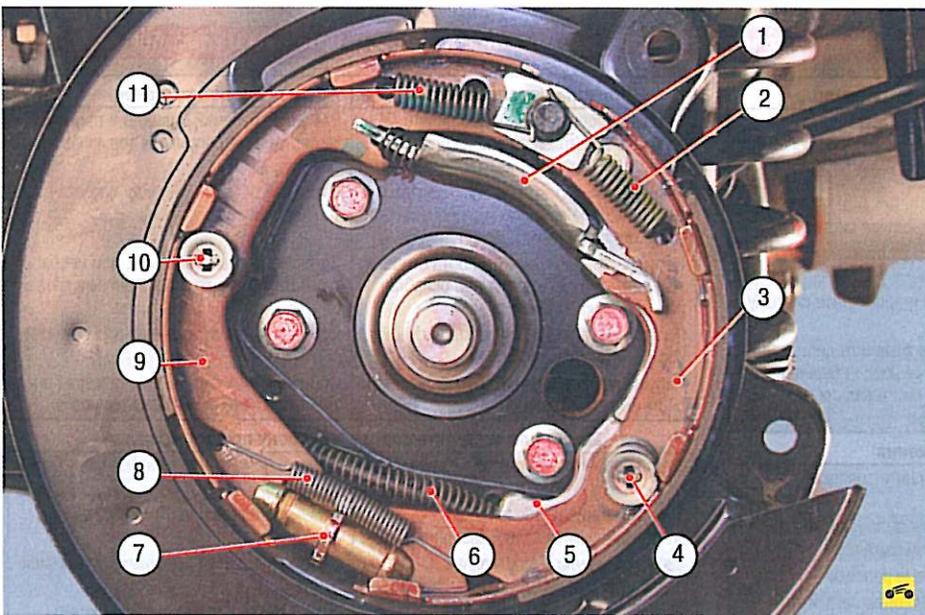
Детали заднего стояночного тормозного механизма: 1 – разжимная планка; 2 – верхняя стяжная пружина задней колодки; 3 – задняя колодка стояночного тормоза; 4, 10 – опорные стойки колодок; 5 – разжимной рычаг привода колодок; 6 – задний трос стояночного тормоза; 7 – регулировочное устройство тормозных колодок стояночного тормоза; 8 – нижняя стяжная пружина колодок; 9 – передняя колодка стояночного тормоза; 11 – верхняя стяжная пружина передней колодки
